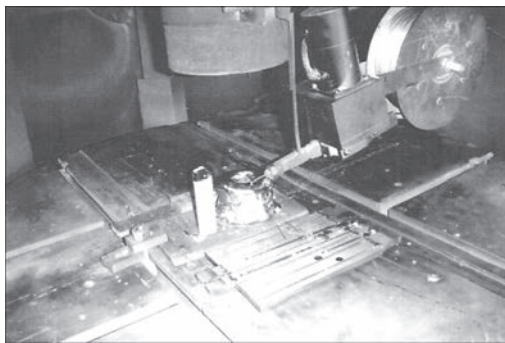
Расположение детали с формой тела вращения и механизма подачи присадочной проволоки в камере электронно-лучевой установки
